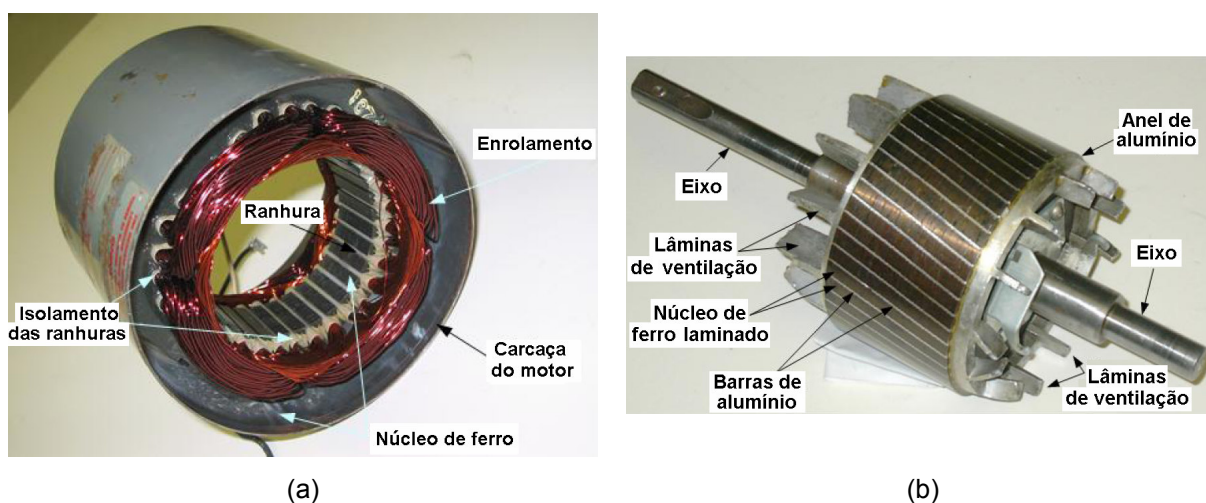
Componentes elétricos básicos de um motor de indução: (a) estator e (b) rotor (adaptado de [14]).
